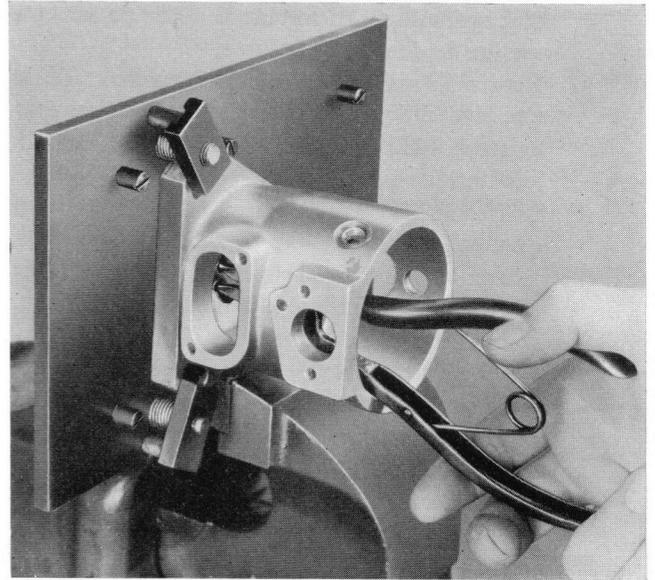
Démontage ou remontage du circlip de positionnement de l'arbre d'entraînement cannelé
